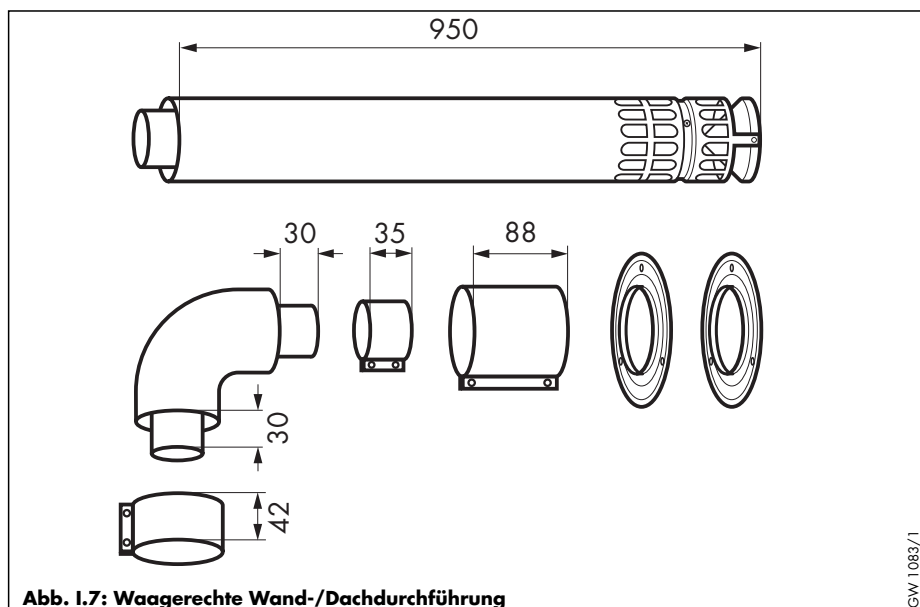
Waagerechte Wand-/Dachdurchführung
